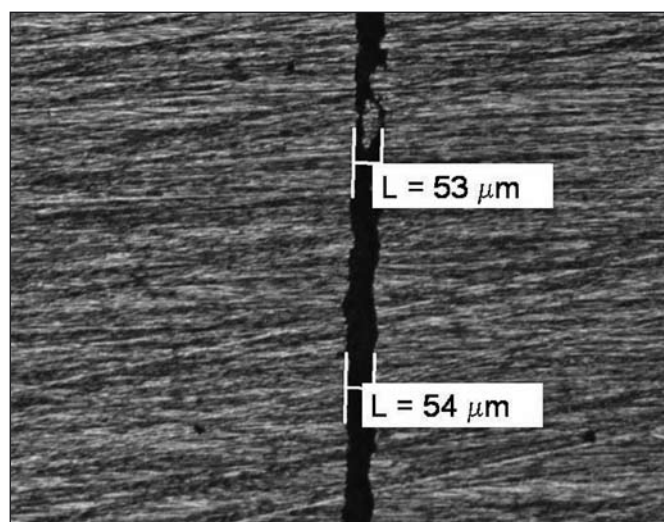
Vyhodnocený lepený spoj – deformovaný distanční drátek
